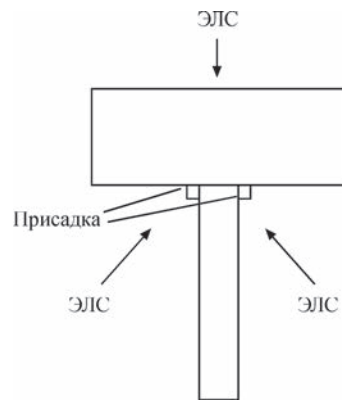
Схема сварки таврового соединения «лопатка-диск» с применением электронного луча для расплавления присадки из стали X3CrNiMo13-4
